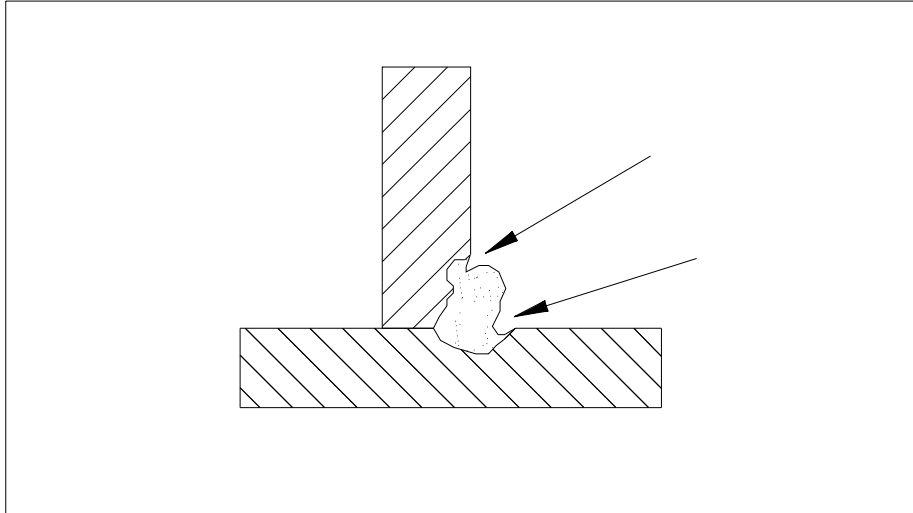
Socavamiento en una soldadura de filete o angular(SOLDADURA, APLICACIONES Y PRACTICAS, Henry Horwitz, P.E.1997, capítulo 22, Pág. 688).
